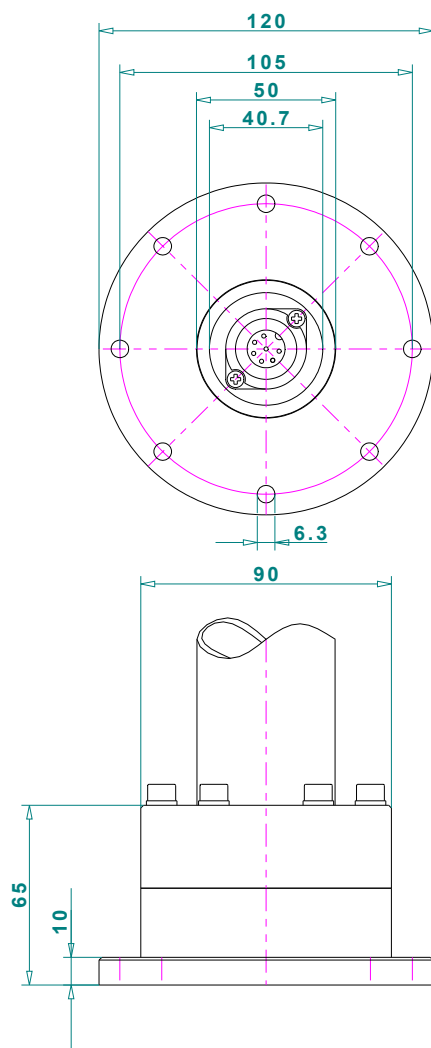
Antenna Unit Mast Flansch (mechanische Abmessungen)
